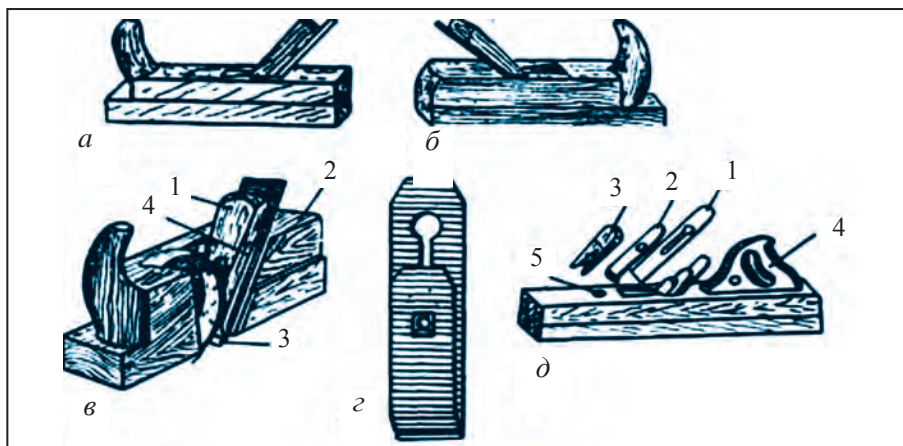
Виды рубанка; *а*) шерхебель; *б*) досочный рубанок; *в*) мушранда: 1 – клин; 2 – колода; 3 – нож; 4 – железный пуштак; *з*) нож с пуштак; *д*) плотный рубанок (жапс ранда): 1 – нож; 2 – пуштак; 3 – клин; 4 – ручка; 5 – кнопка кования.
